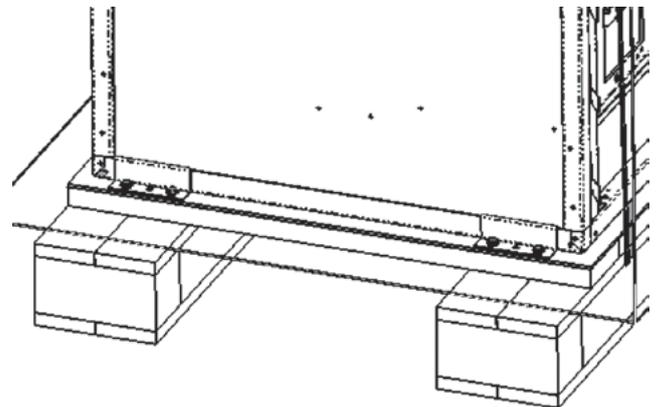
Platten zur Montage außen am Schaltfeld 750 mm
